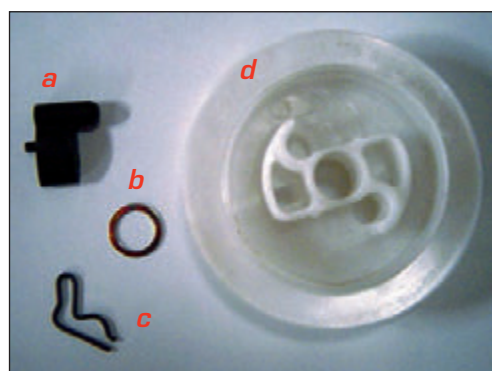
Despiece del dispositivo de arranque. a) Trinquete. b) Arandela. c) Clip. d) Polea
